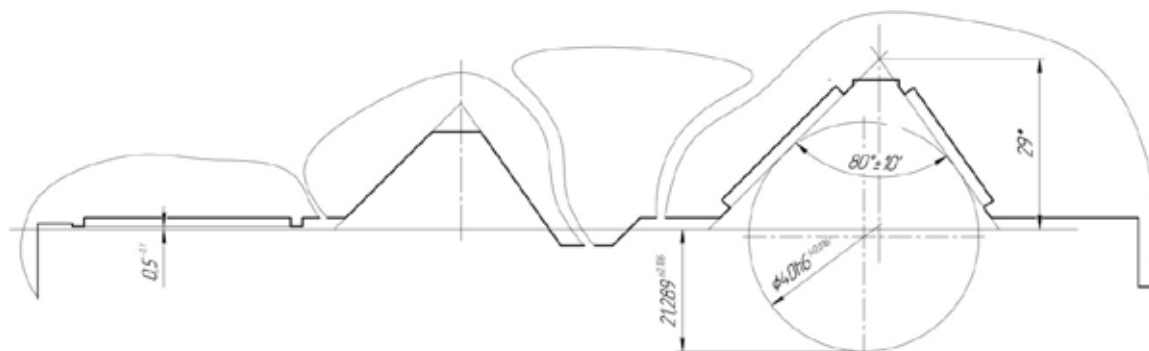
Базовые поверхности суппорта, контактирующие с направляющими станины станка НТ-250И под суппорт
